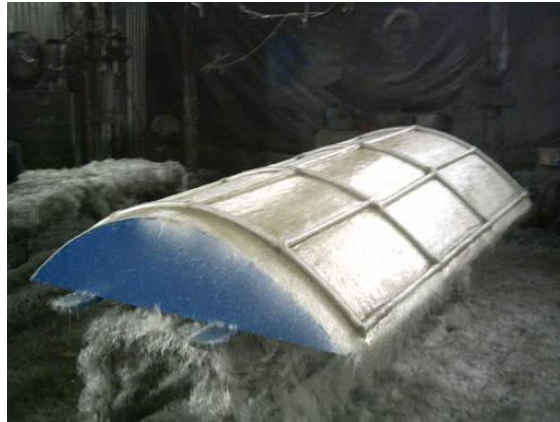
Fijación de los refuerzos de aluminio con fibra de vidrio.
